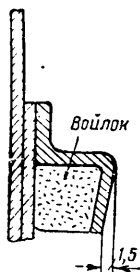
Желоб для войлочного уплотнения корпуса ящика высоковольтного предохранителя
